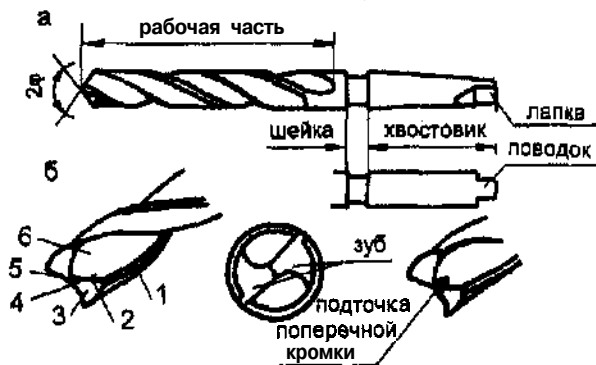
Спиральное сверло и его элементы: 1 — ленточка; 2 — режущая кромка; 3 — задняя поверхность; 4 — передняя поверхность; 5 — поперечная кромка; 6 — канавка
